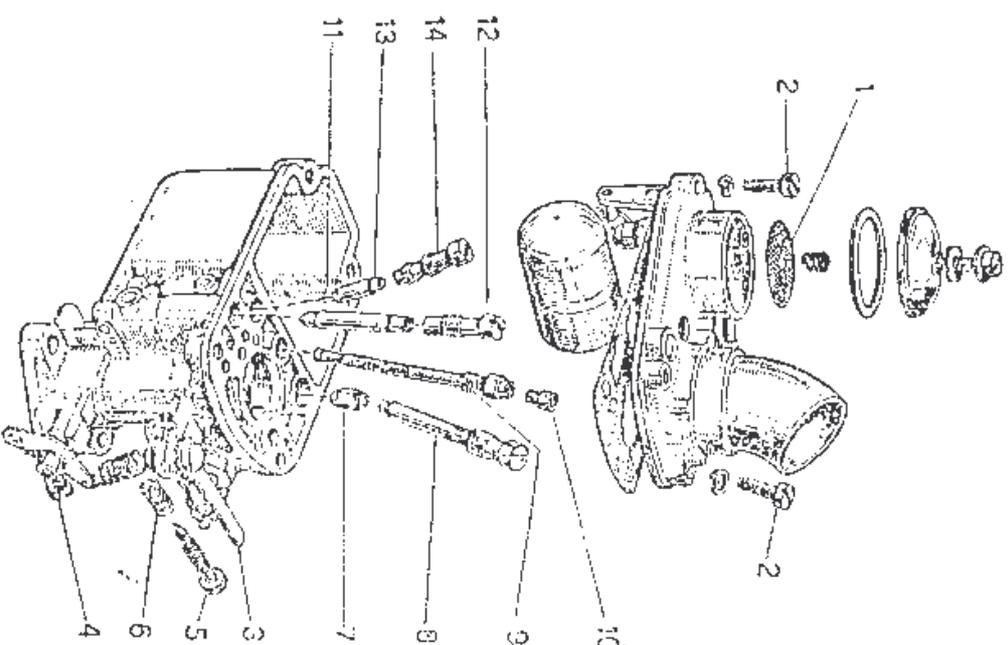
Carburatore Weber 22 DZM smontato per la pulizia
